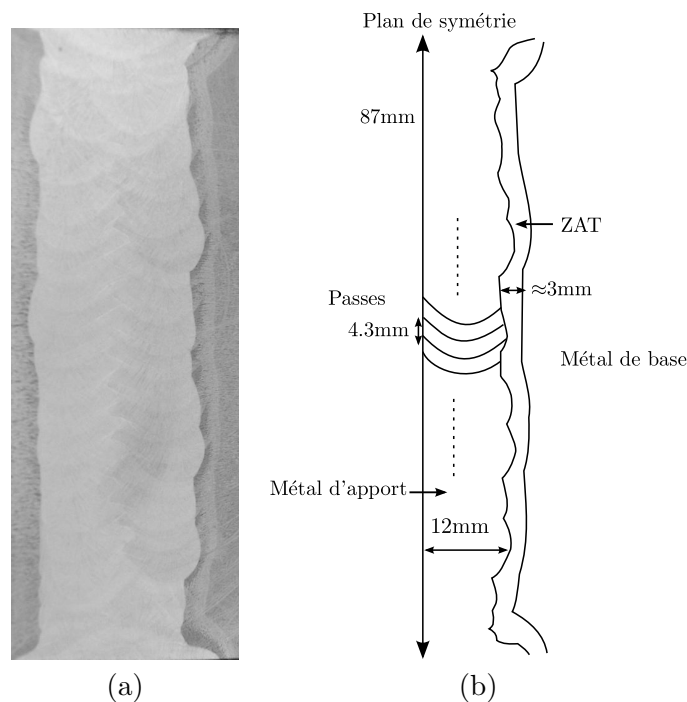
(a) Macrographie du joint soudé dans le plan T-TC après une attaque au Nital (hauteur du joint soudé : 87mm), (b) représentation schématique et dimensions des différentes zones.
